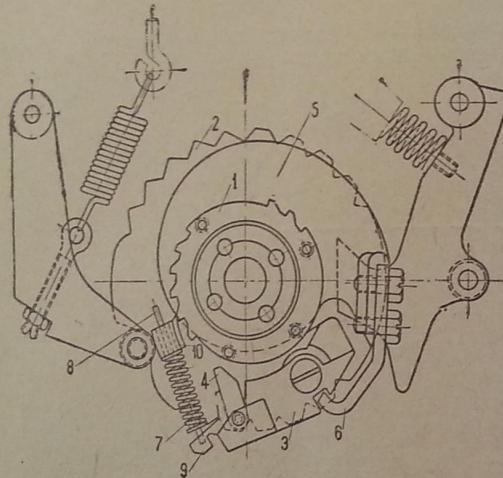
Механизм блокировки коробок погашений контроллера ДТ-41.
